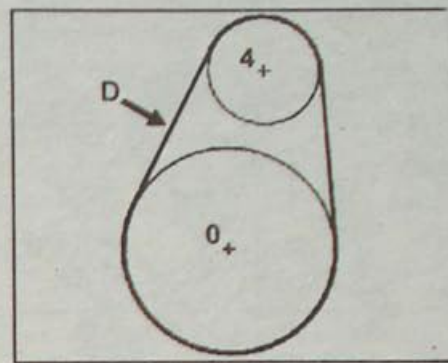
Расположение на шкивах ремня привода вспомогательного оборудования двигателя Z:
